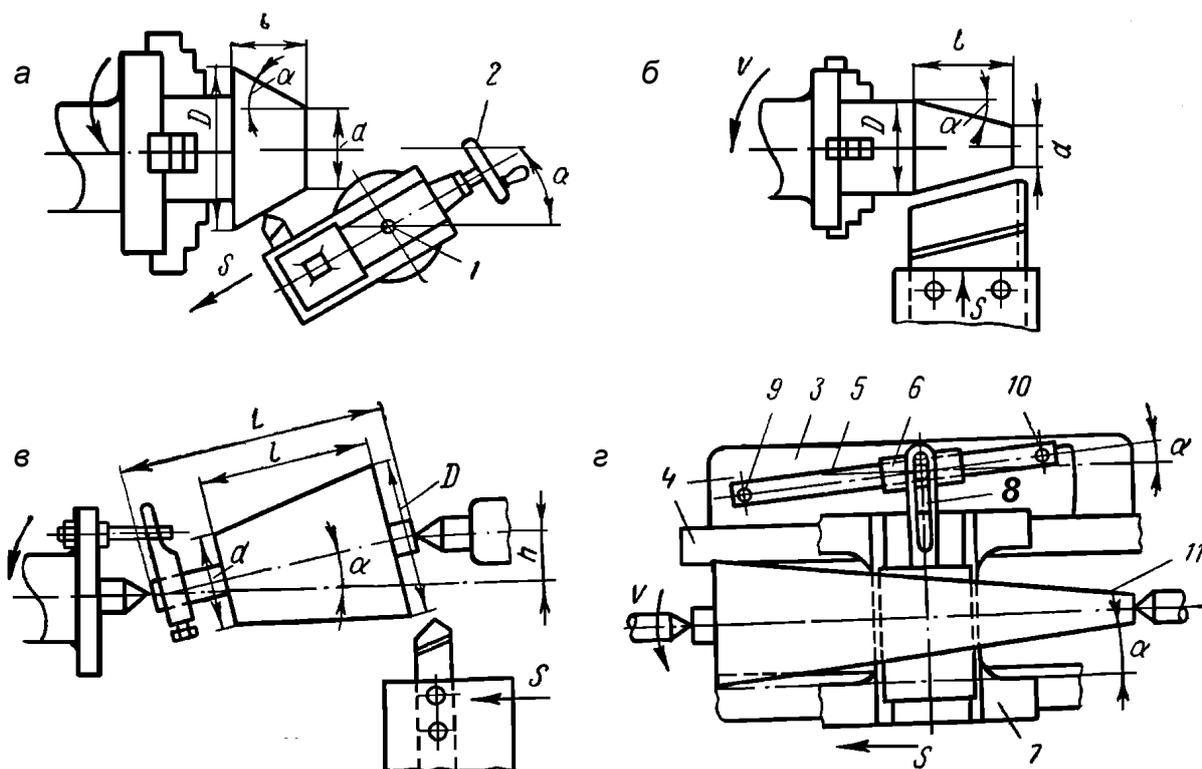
Схема точения конусов: а – поворотом верхних салазков суппорта; б – широким резцом; в – смещением центра задней бабки; г – при помощи копировальной линейки; 1 – ось; 2 – рукоятка; 3 – кронштейн; 4 – станина; 5 – линейка; 6 – ползун; 7 – суппорт; 8 – тяга; 9, 10 – болт; 11 – деталь
